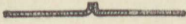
Schweißnaht für Bleche unter 1 mm Stärke.
